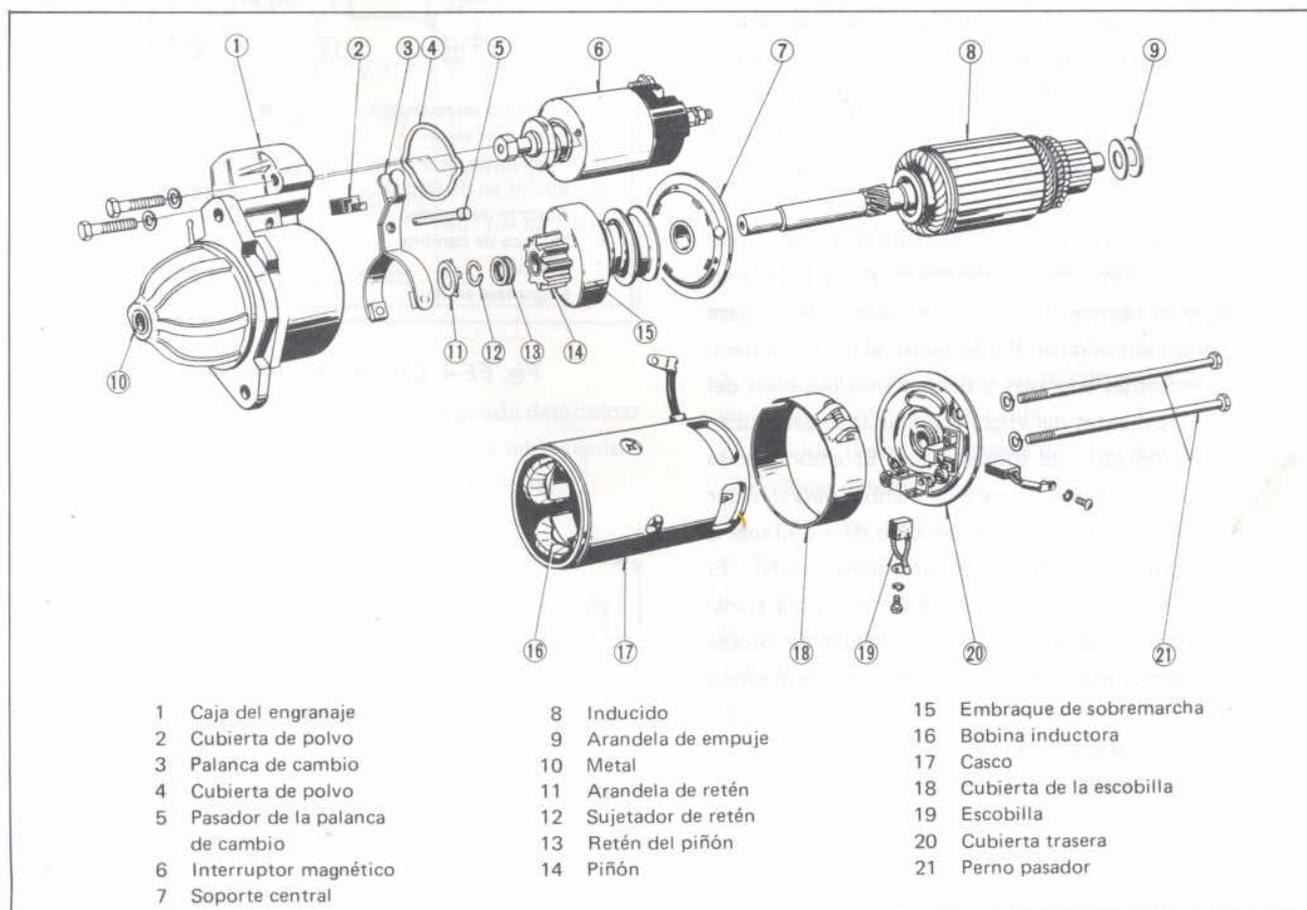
Vista desmontada del motor de arranque (S114-87L)
